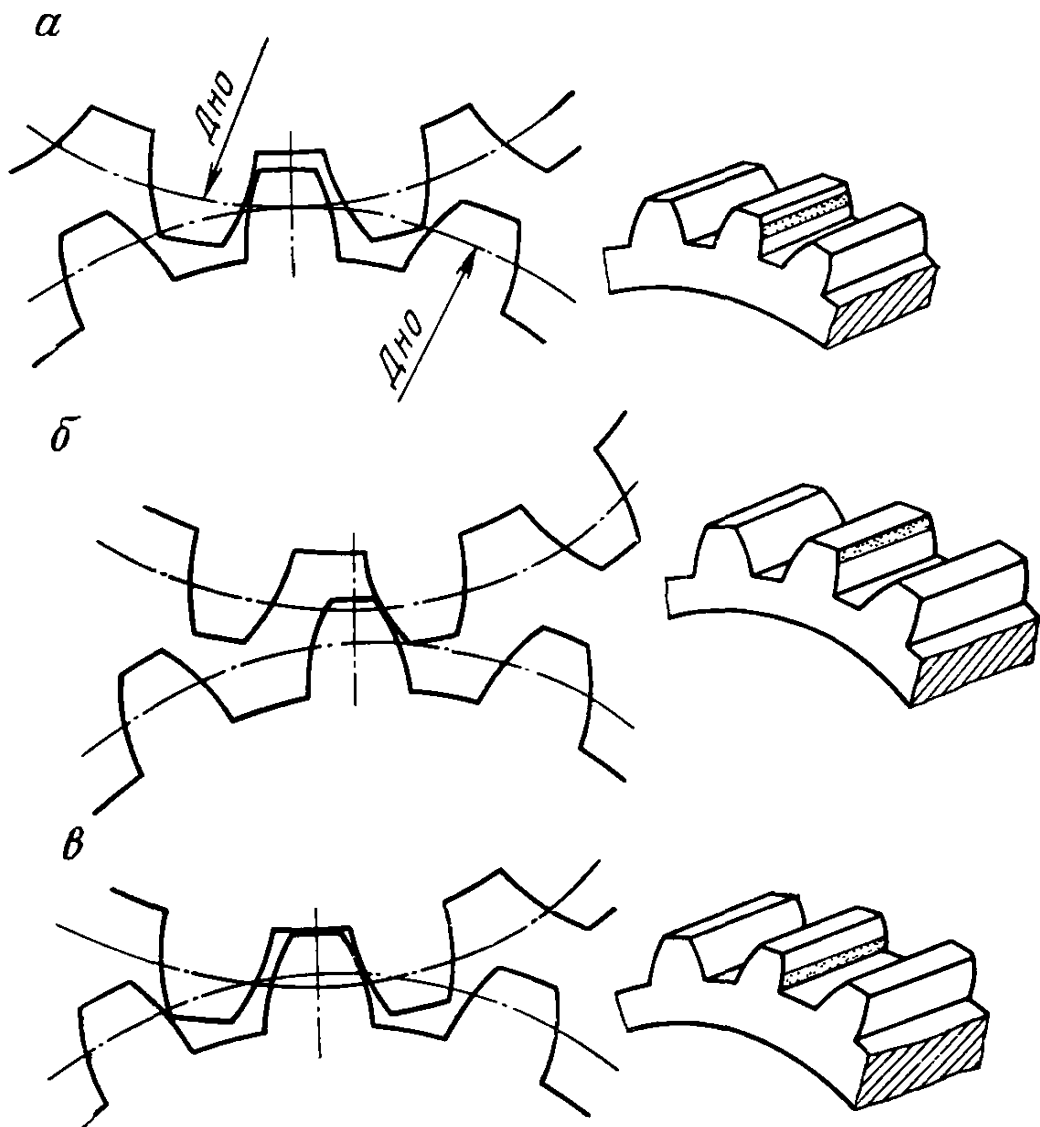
Виды зацеплений цилиндрических зубчатых колес:
